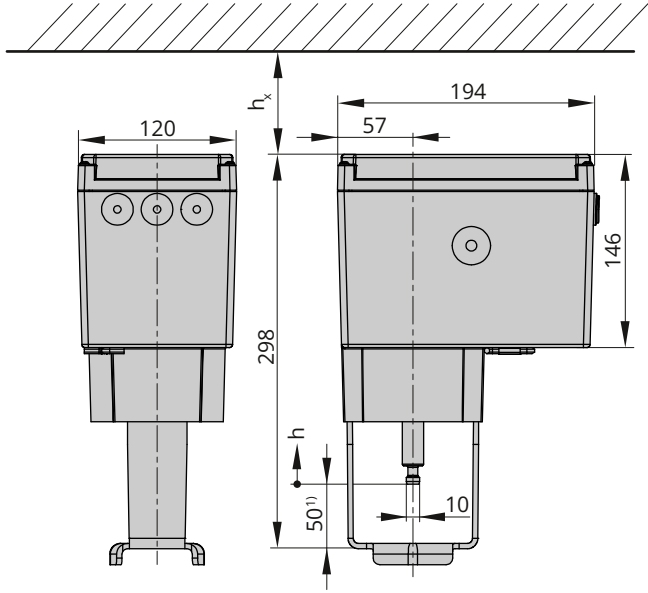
mm cinsinden boyutlar · Tip 3374-10, -11, -21 ve -31 (form B)
